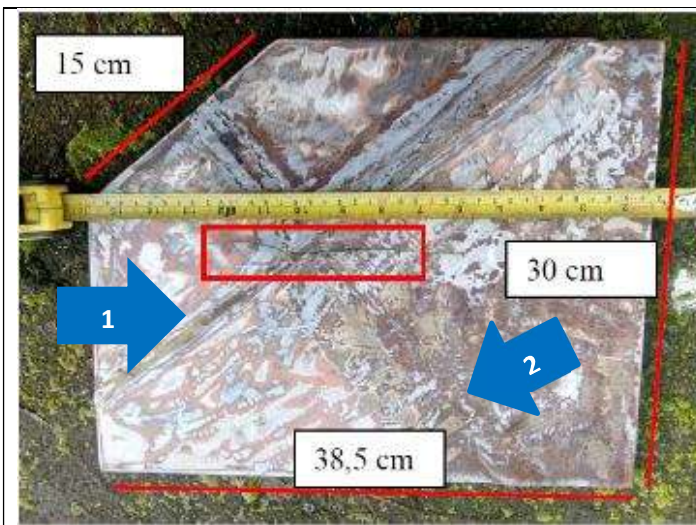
En la fotografía se observa las dimensiones de la plancha analizada, con presencia de una grieta de aproximadamente 220 mm de longitud en el centro de ésta (recuadro rojo). Se observan además tres cordones de soldadura: uno con gran sobre-monta (cordón de flecha azul 1) con aporte por ambos lados (bisel en X) y dos cordones paralelos (cordones de flecha azul 2) muy a ras de la plancha y aporte por un solo lado (bisel en v).
